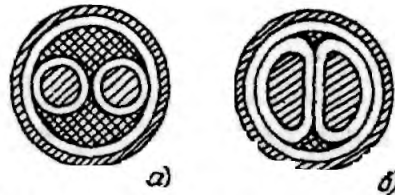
Двухжильные кабели с круглыми (а) и сегментными (б) жилами
